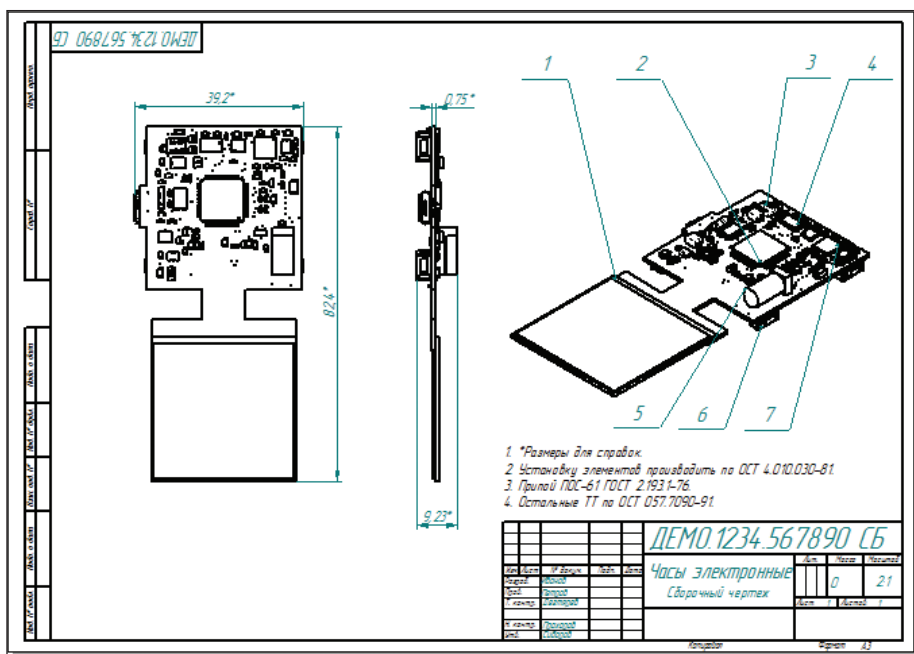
Сборочный чертеж печатной платы в Solid Edge
